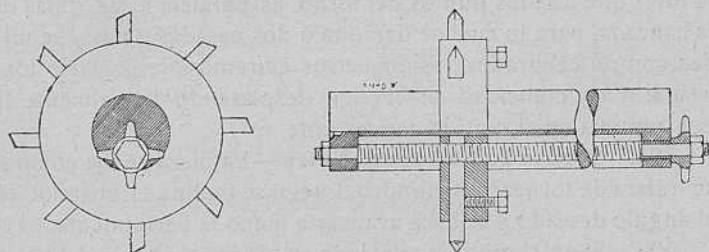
Torneador para mandrilar, con dispositivo para hacer avanzar la herramienta.
